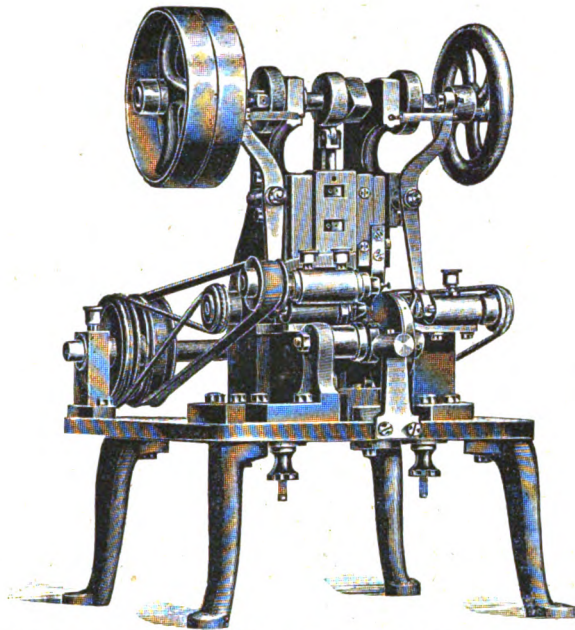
Maschine zum Einfräsen der Schlitz und Bohren der Löcher für die Finierstifte.
